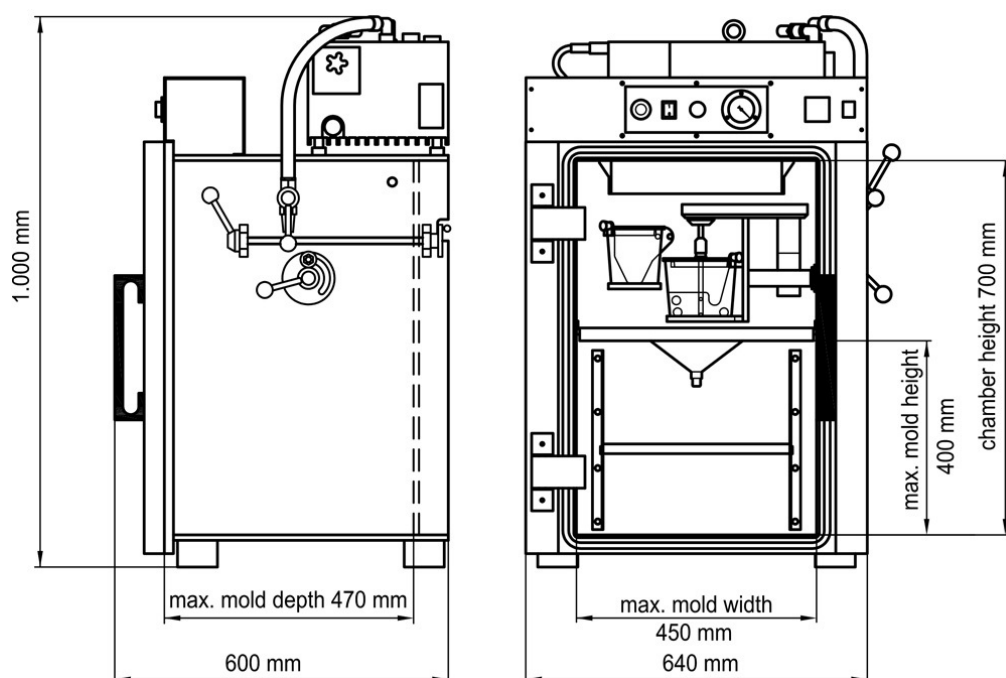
Основные размеры установки вакуумного литья МК-MINI
